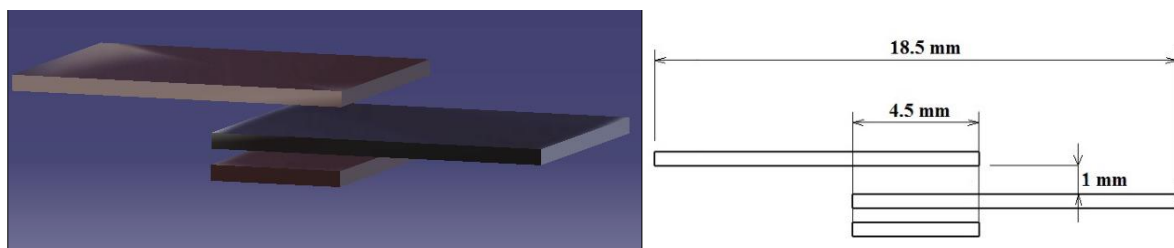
Installation et géométrie du système de soudage des plaques
